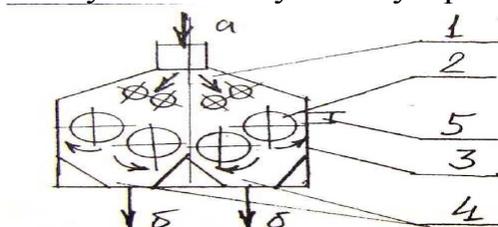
Вальцовый станок: 1 - приёмно-питающее устройство; 2 - мелющие вальцы; 3 - корпус; 4 - выпускное устройство; 5- система привалки валцов; а- исходный продукт.
